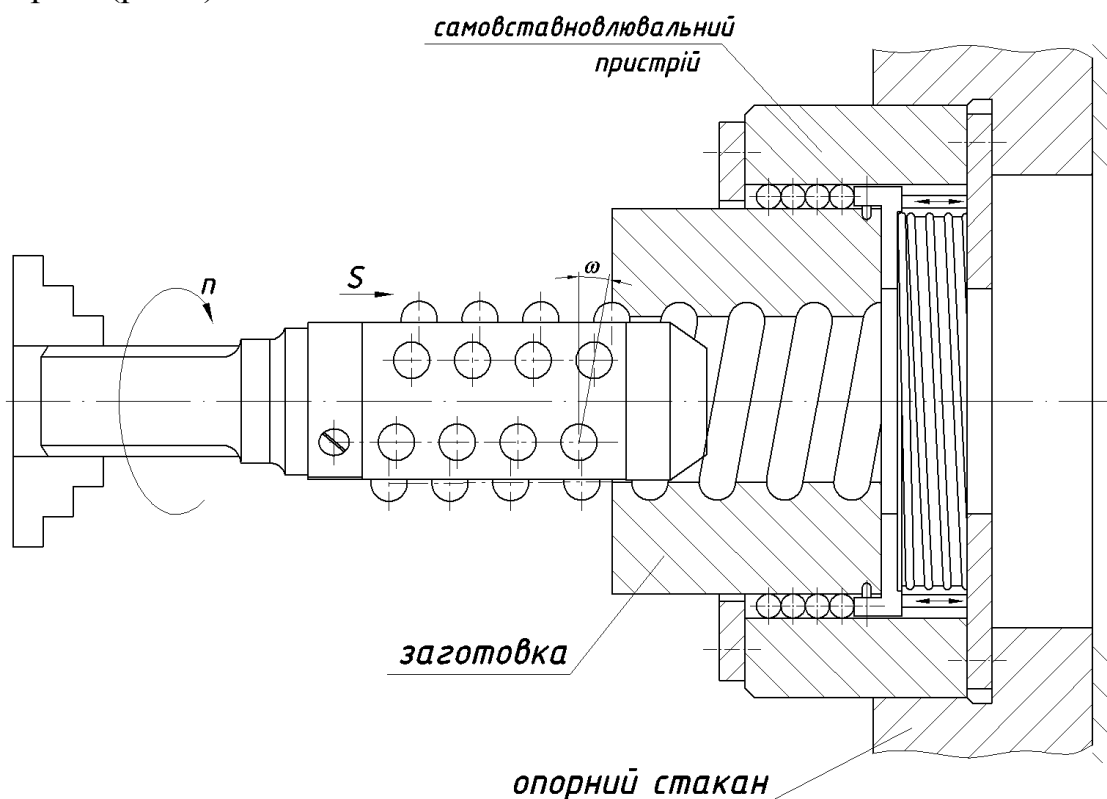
Самовстановлювальний пристрій для дорнування внутрішніх гвинтових напівкруглих канавок з кріпленням заготовки в пристрої
